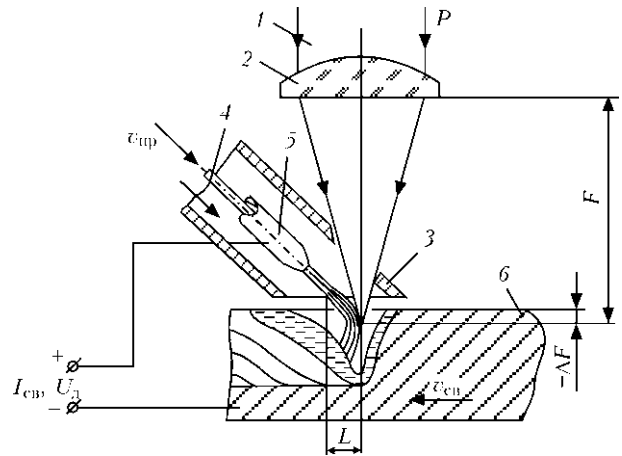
Схема проведения экспериментов по гибридной лазерно-дуговой сварке алюминиевых сплавов: 1 — лазерное излучение мощностью P ; 2 — фокусирующий объектив с фокусным расстоянием F ; 3 — защитное сопло; 4 — присадочная проволока; 5 — медный токоподводящий муфштук; 6 — образец; ΔF — заглабление горловины каустика излучения относительно поверхности образца; L — расстояние между концом плавящегося электрода и осью лазерного излучения
